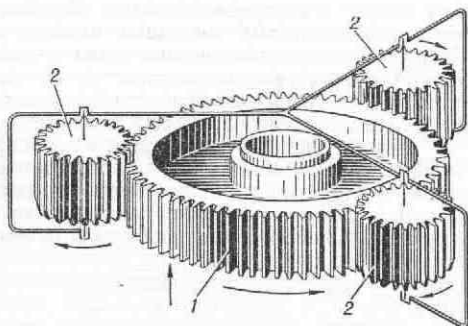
Схема деформационного упрочнения зубчатого колеса по всему профилю зубьев; 1 — изделие (упрочняемое колесо); 2 — инструменты (зубообкатные валки).
